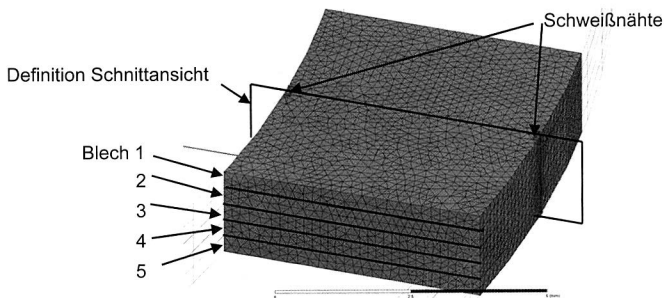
Finite-Elemente-Modell, fünf Bleche mit Schweißnähten, Vernetzung und Definition der Schnittansicht
